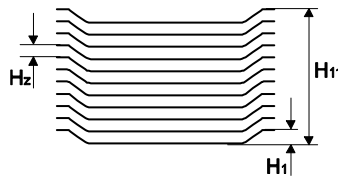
Altezza di pila intermedia H_z per 11 pezzi di stoviglie
